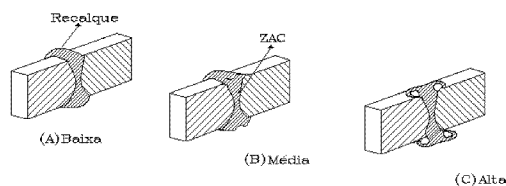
Efeito da Energia do Volante sobre a Geometria da Solda na Soldagem por Inércia.
